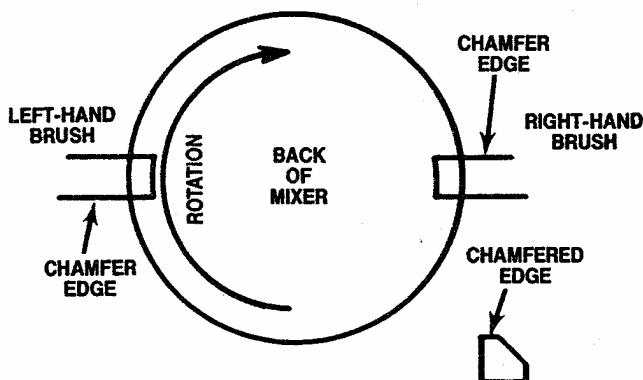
Ausrichtung der Bürstenhalter-Einsätze, von hinten auf das Motorgehäuse gesehen.
